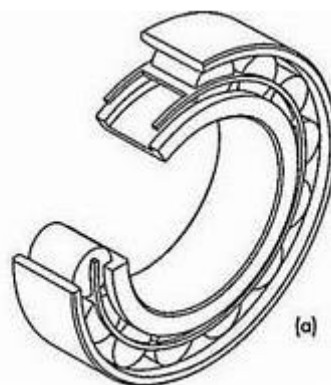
Rodamiento de rodillos cilíndricos.
